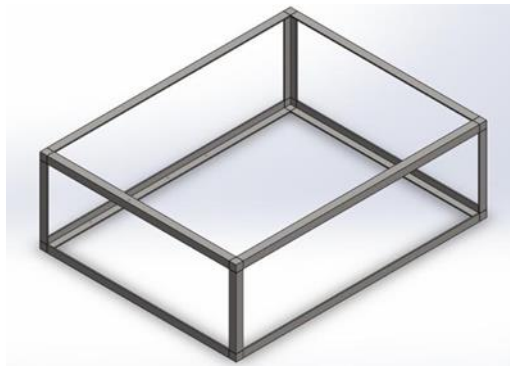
Diseño del cernidor realizado en SolidWorks
